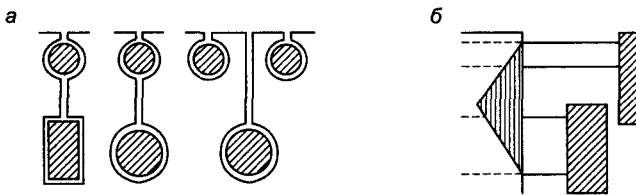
Двухклеточный двигатель: а — пазы ротора; б — короткозамыкающие кольца ротора
